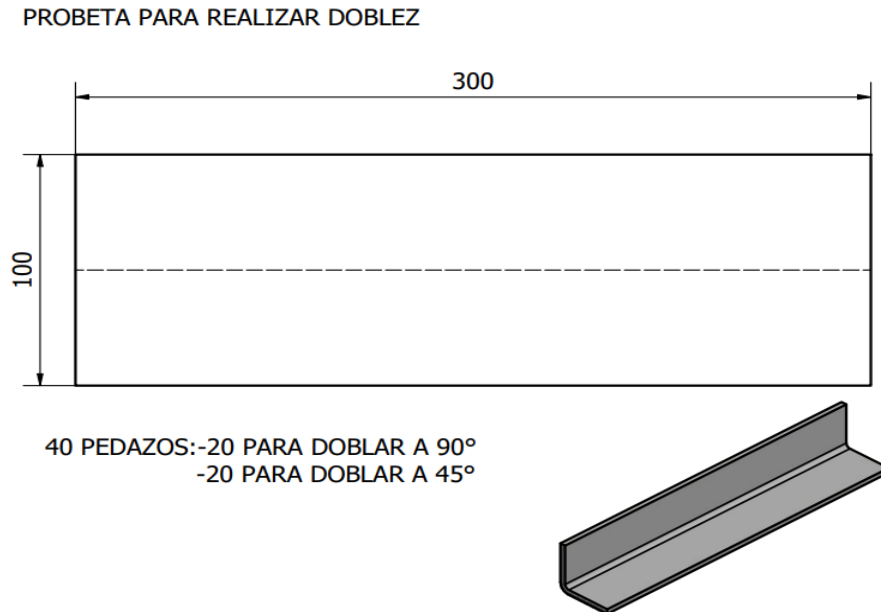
Dimensiones de corte de probetas para realizar el doblar (fuente propia)
